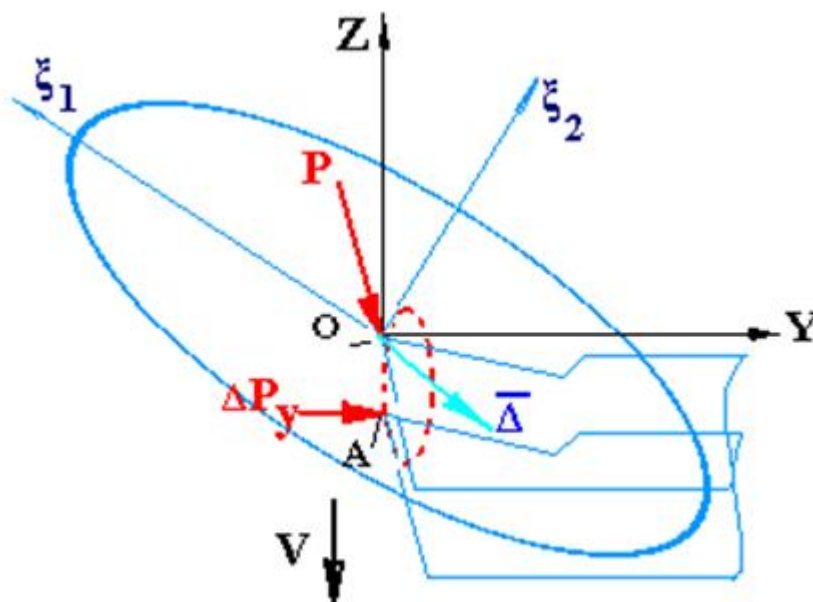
Схема формирования колебательных движений вершины резца, возникающих с участием координатной связи
